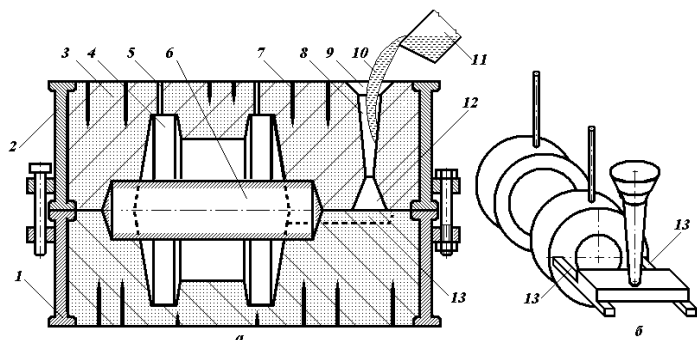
Схема процесса литья в разовые съемные формы: а – принципиальная схема; б – отливка после выбивки; 1, 2 – нижняя и верхняя опоки; 3 – форма; 4 – полость формы; 5 – выпор; 6 – литейный стержень; 7 – вентиляционный канал; 8 – вертикальный канал (стояк); 9 – литниковая чаша (воронка); 10 – расплавленный металл; 11 – ковш; 12 – шлакоуловитель; 13 – горизонтальные каналы (питатели)
